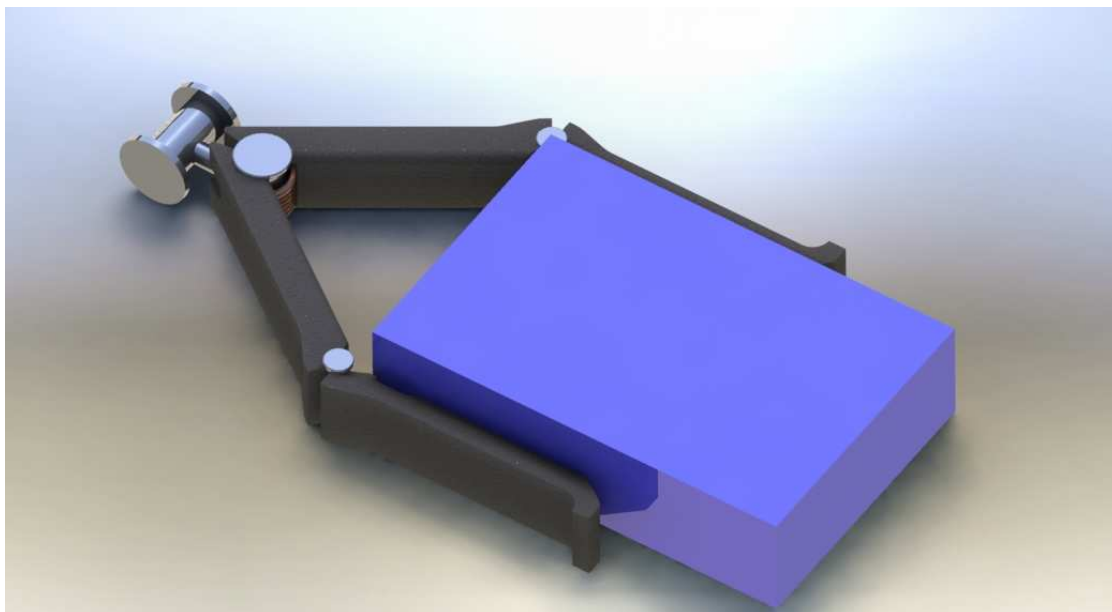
imbocco e presa di un oggetto di sezione rettangolare.
